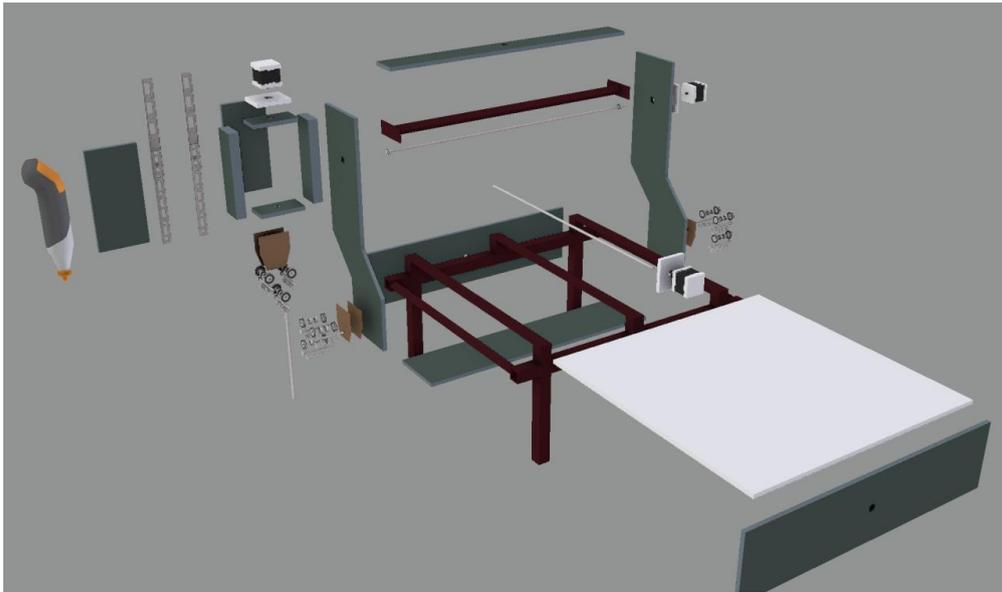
3 : Vue éclatée de la machine à réaliser.
